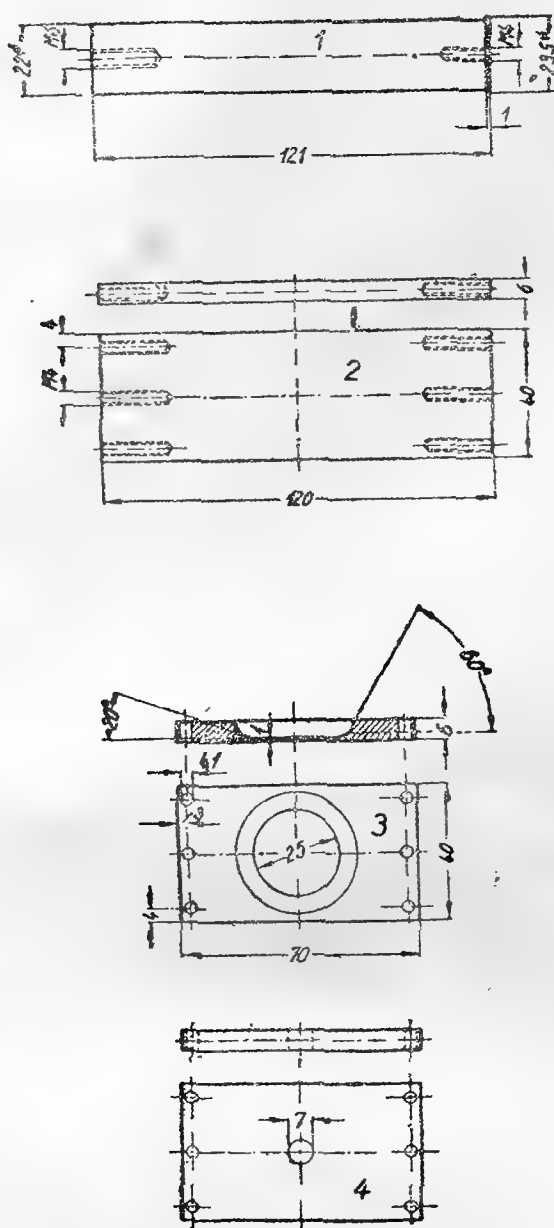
Железные детали магнитной системы: 1—сердечник, 2—боковые пластинки скобы, 3—верхняя пластинка с отверстием в середине для звуковой катушки динамика, 4—нижняя пластинка скобы
